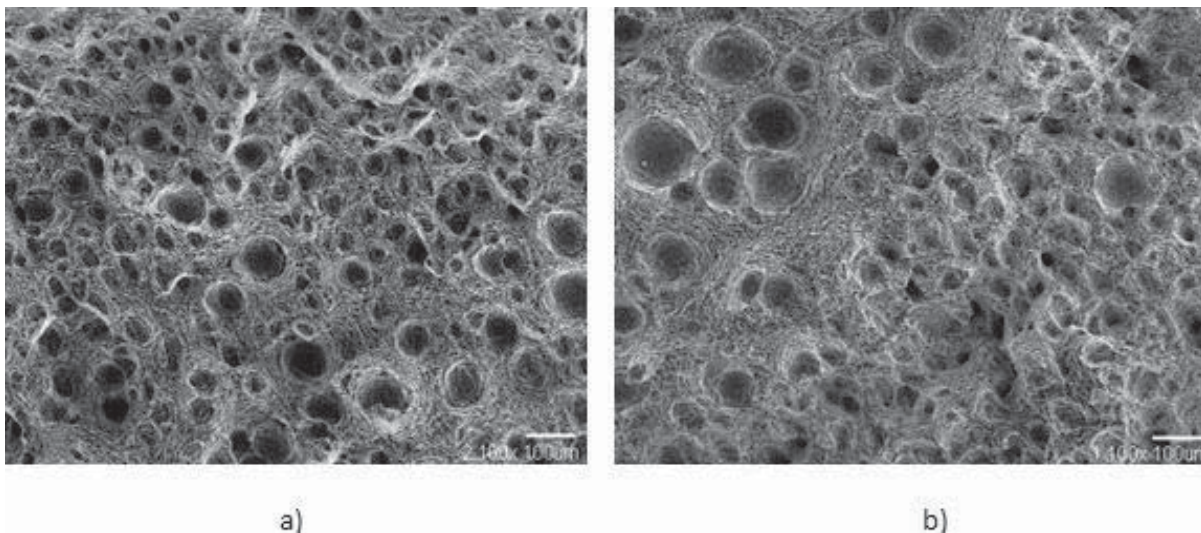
Fractura de la soldadura, a) 401.4 J/mm, b) 736 J/mm
